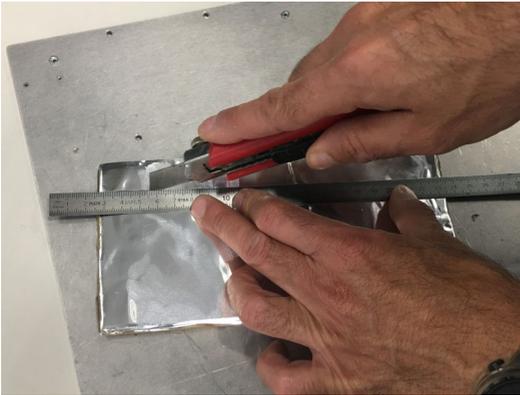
Découpe de l'ABM75 aux dimensions de la zone du ou des capteur(s)
